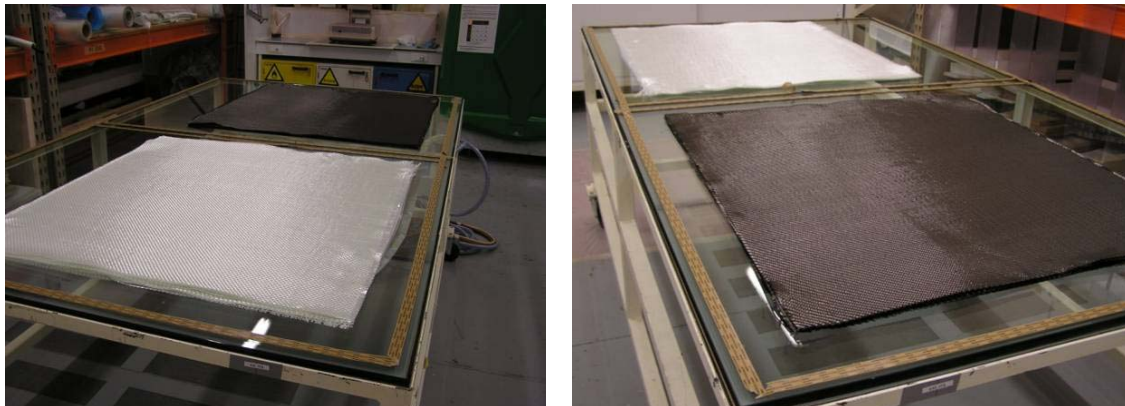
Tissu a) Verre et b) carbone déposé sur un moule en verre.
